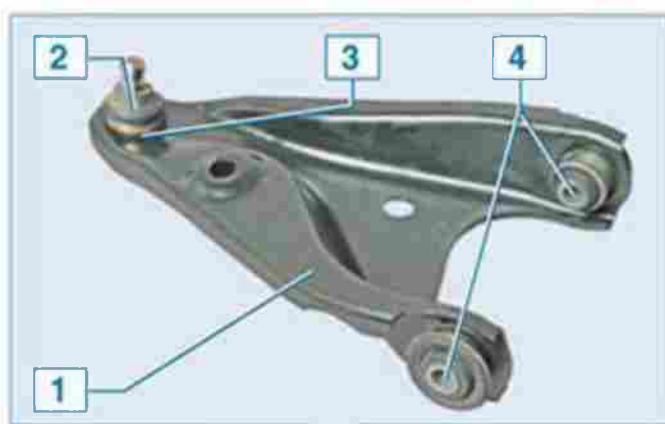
Рычаг передней подвески: 1 - рычаг; 2 - чехол шаровой опоры; 3 - шаровая опора; 4 - сайлент-блок.
